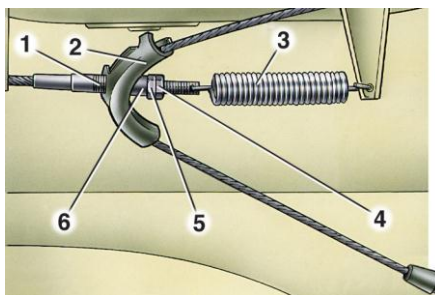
Регулировочный механизм тросового привода стояночного тормоза: 1 – передний трос; 2 – направляющая заднего троса; 3 – оттяжная пружина переднего троса; 4 – контргайка; 5 – регулировочная гайка; 6 – распорная втулка
